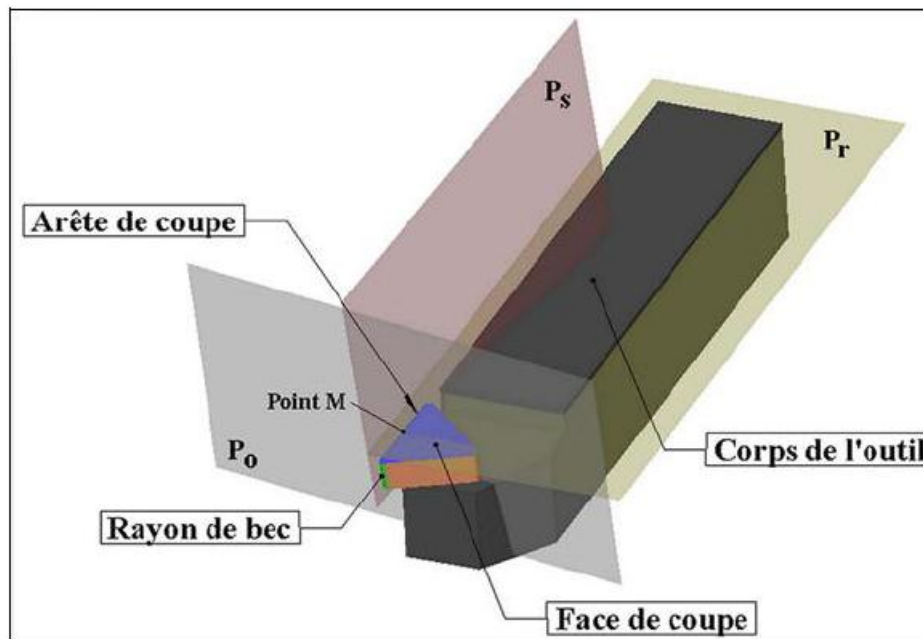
Définition basique d'un outil de coupe de tournage
